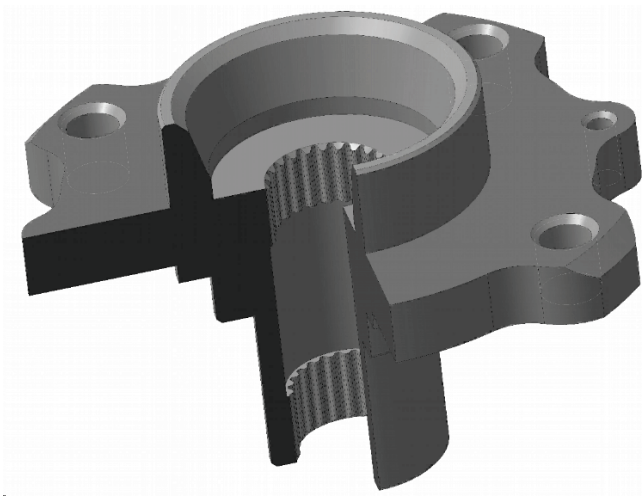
Маточина колеса з внутрішніми шліцьовими елементами
